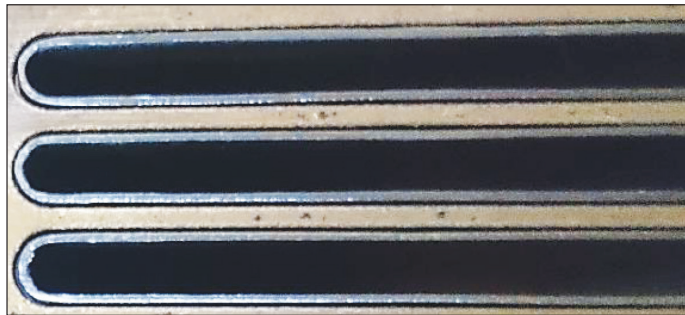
Внешний вид зазоров между трубками и трубной доской
